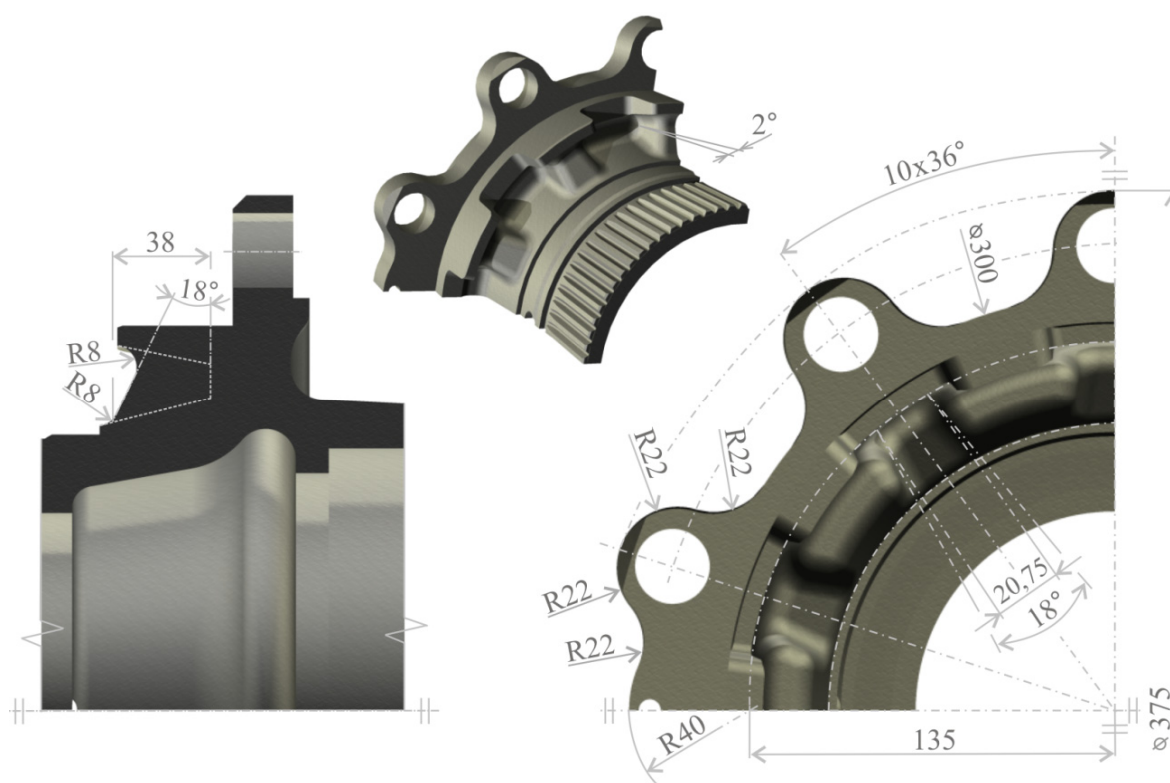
b – Vnější pohled na původní a upravený prototyp náboje diskových kol
